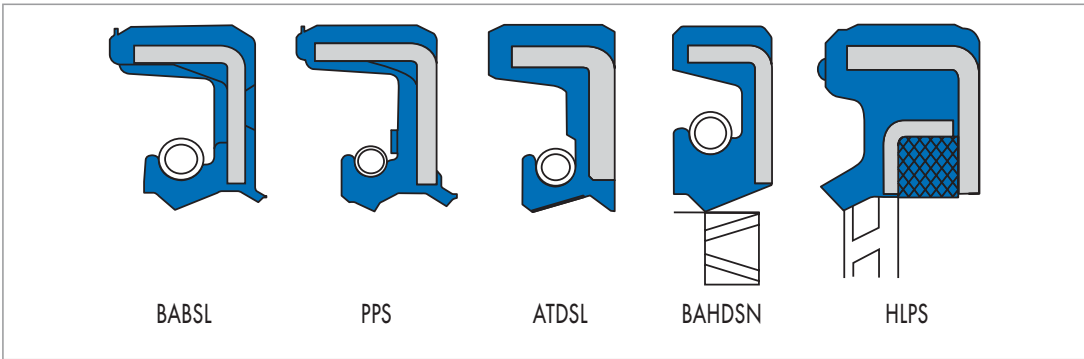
Bauformen für druckbeaufschlagbare Simmerringe
